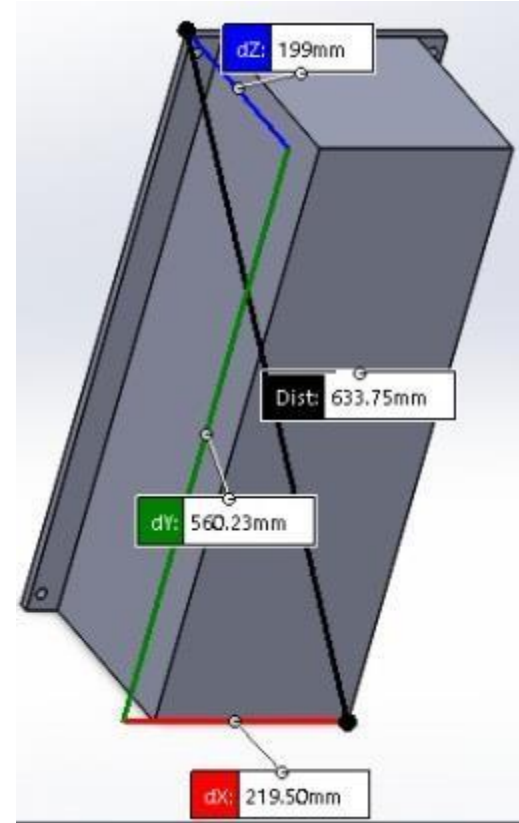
y 75: diseño y dimensiones de carcasa de pistón
